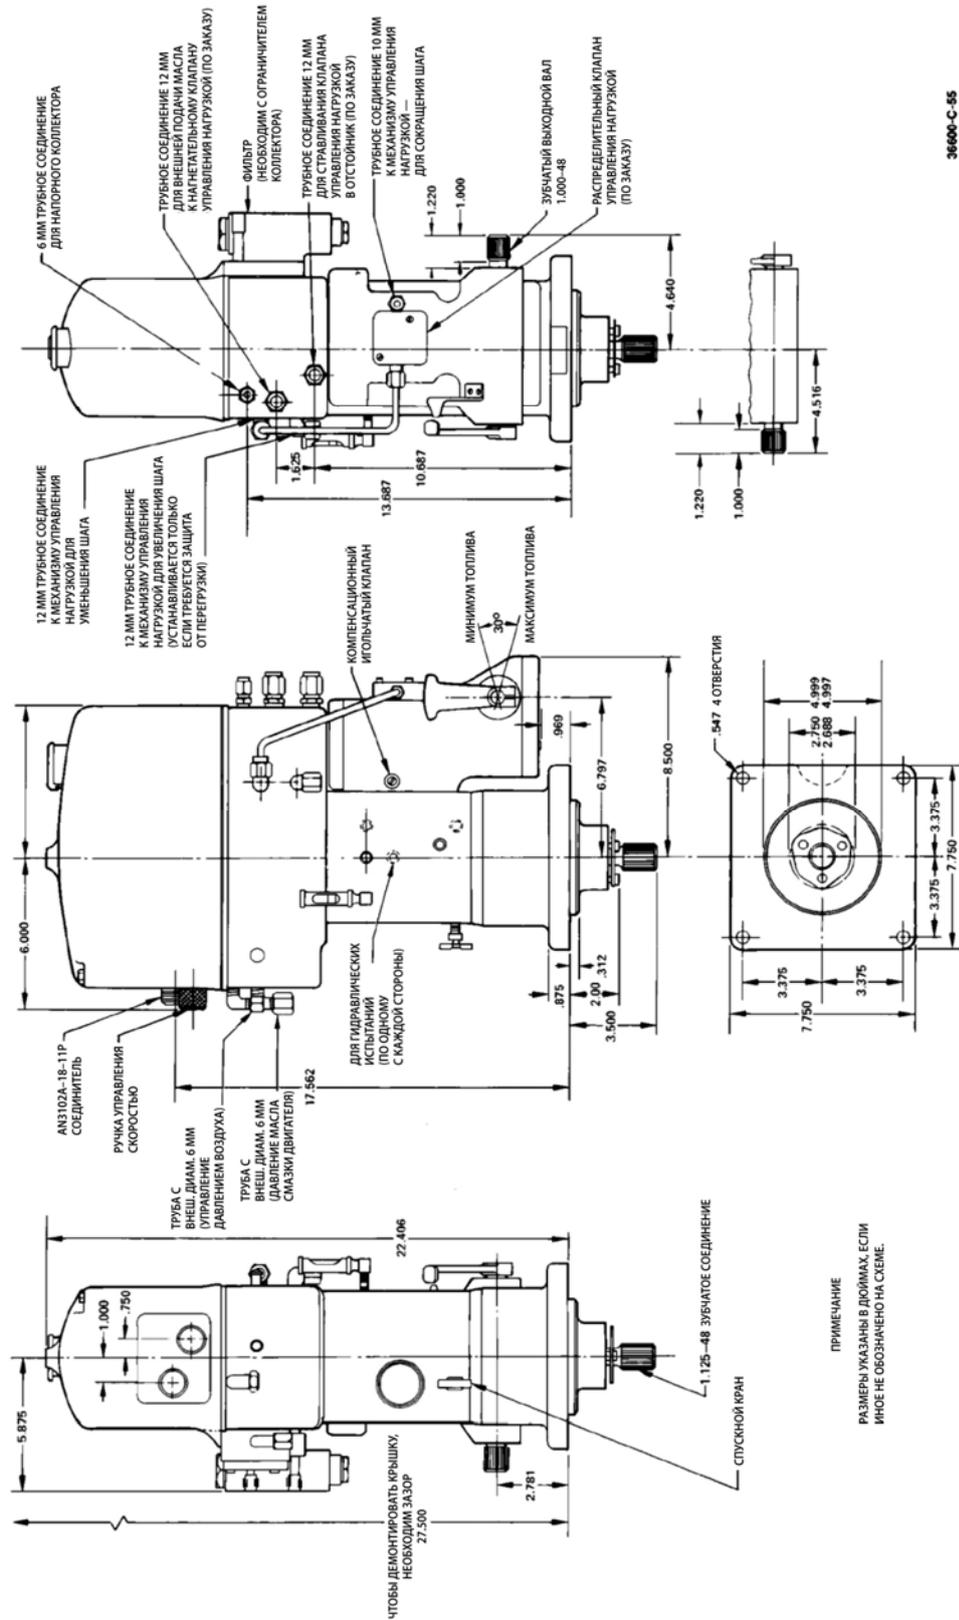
Габаритный чертеж PGA с вращающимся сервоприводом (16 Дж) и базой UG-40 (не использовать в конструировании)
